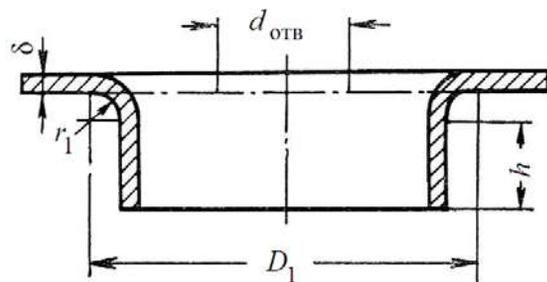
Соотношение основных размеров детали на проведение отбортовки
